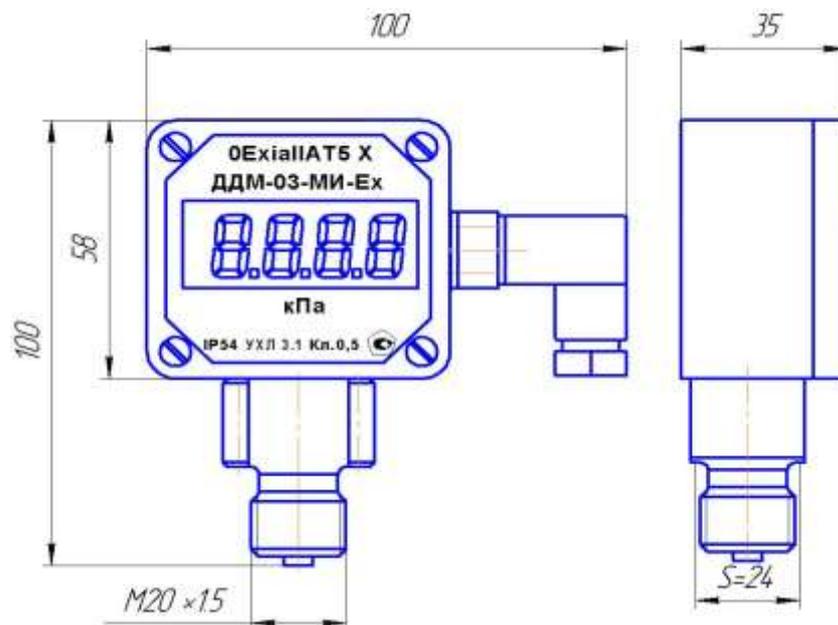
Габаритные и присоединительные размеры датчиков ДДМ-03-xx-ДИ-МИ-Ех
